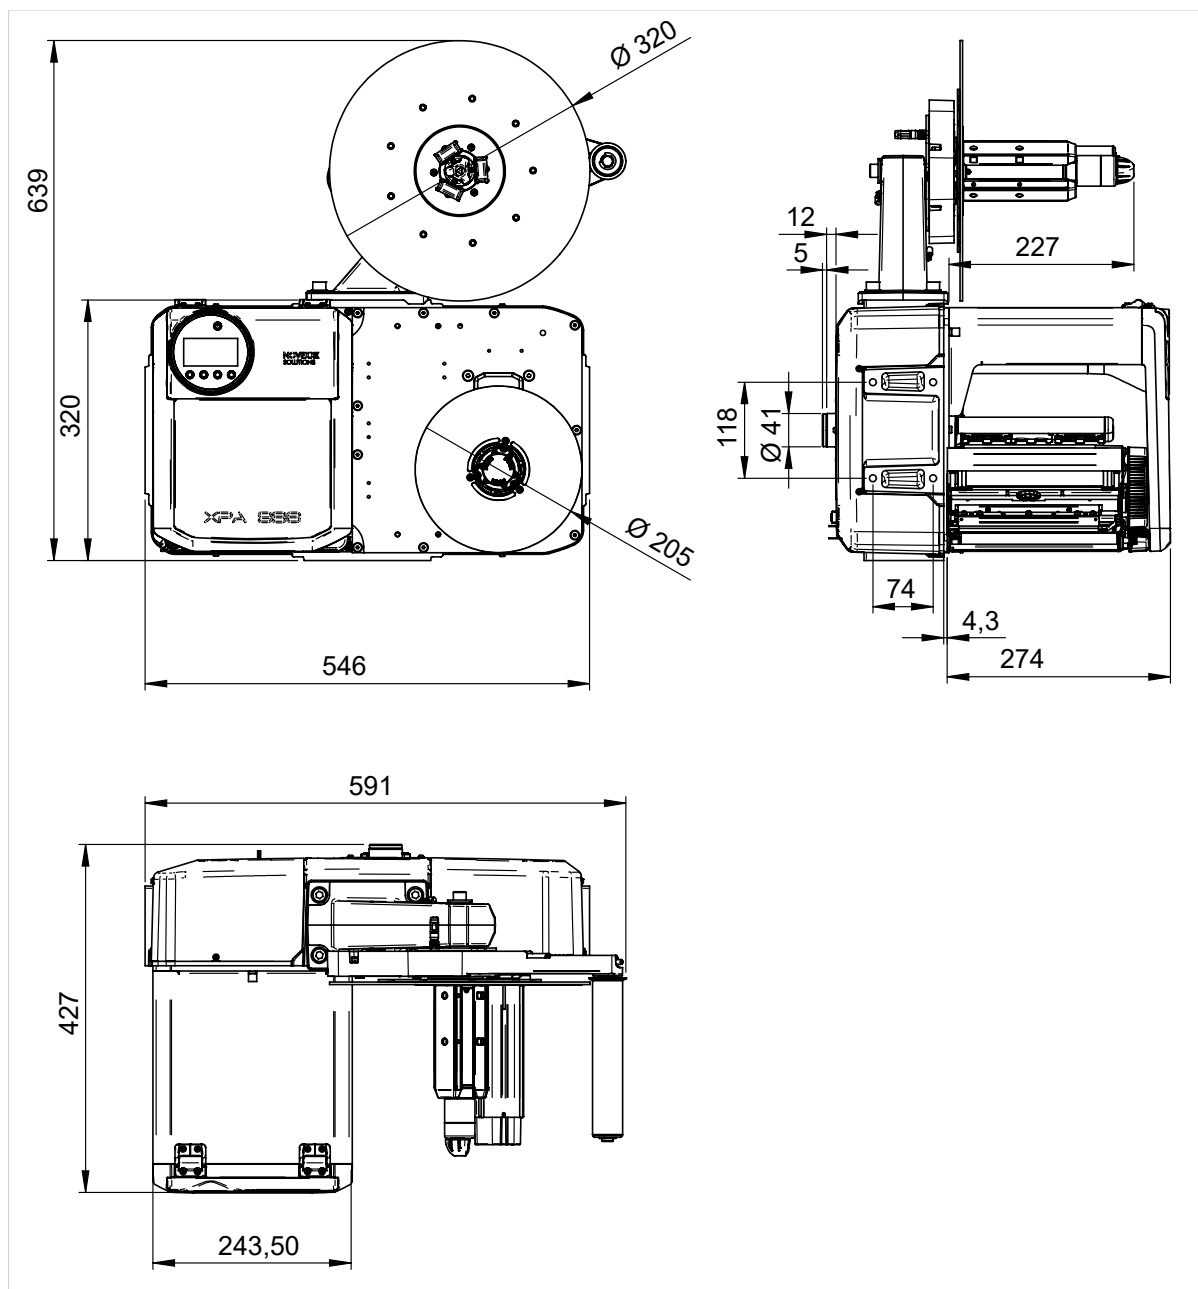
Dimensiones del XPA 936 LH con desenrollador Pro 300.
